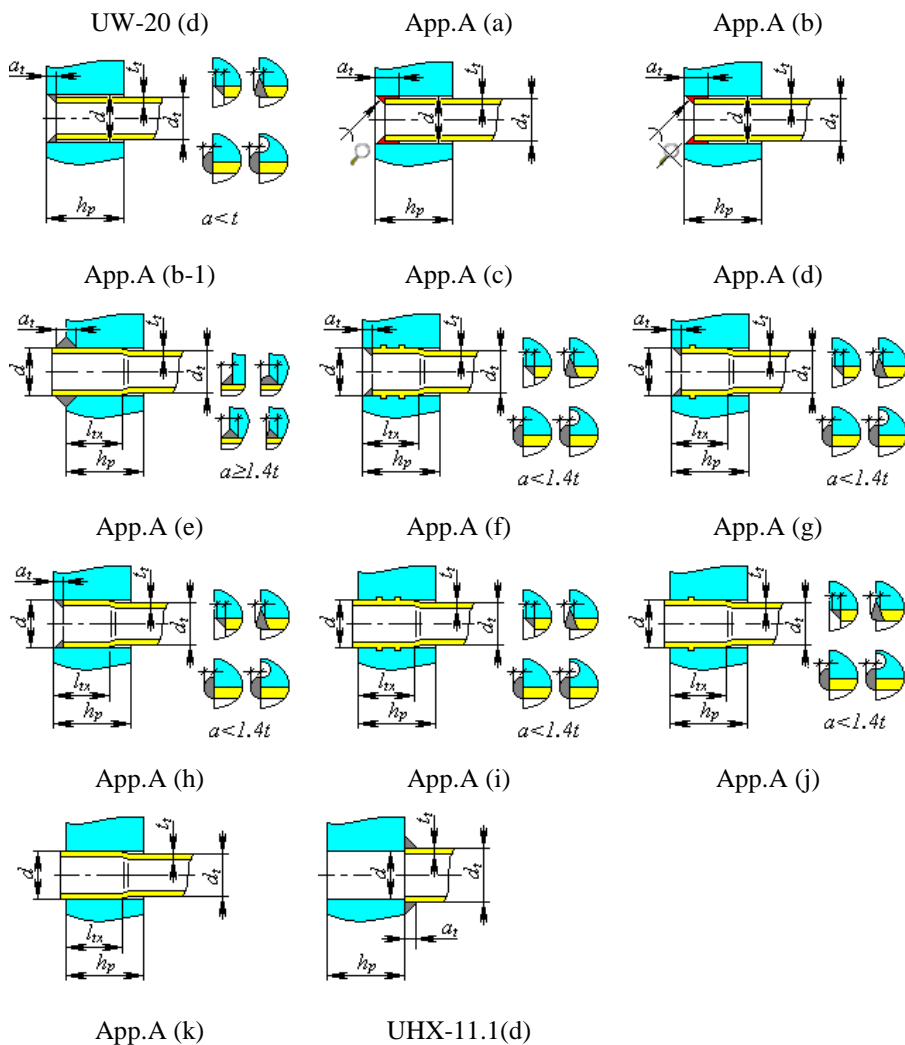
Крепление труб в решетке по ASME VIII-1
